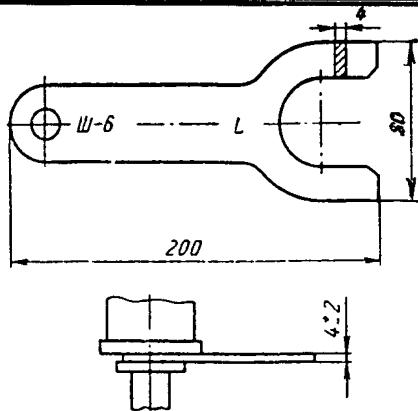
Шаблон Ш-6 для контроля зазора механизма поворота замедлителя КВ
